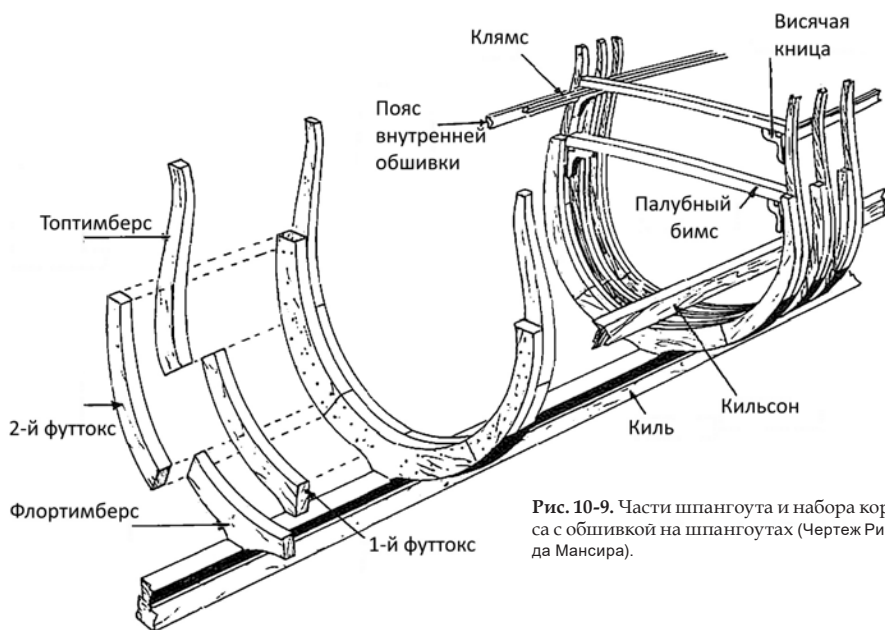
Части шпангоута и набора корпуса с обшивкой на шпангоутах (Чертеж Ричарда Мансира).
